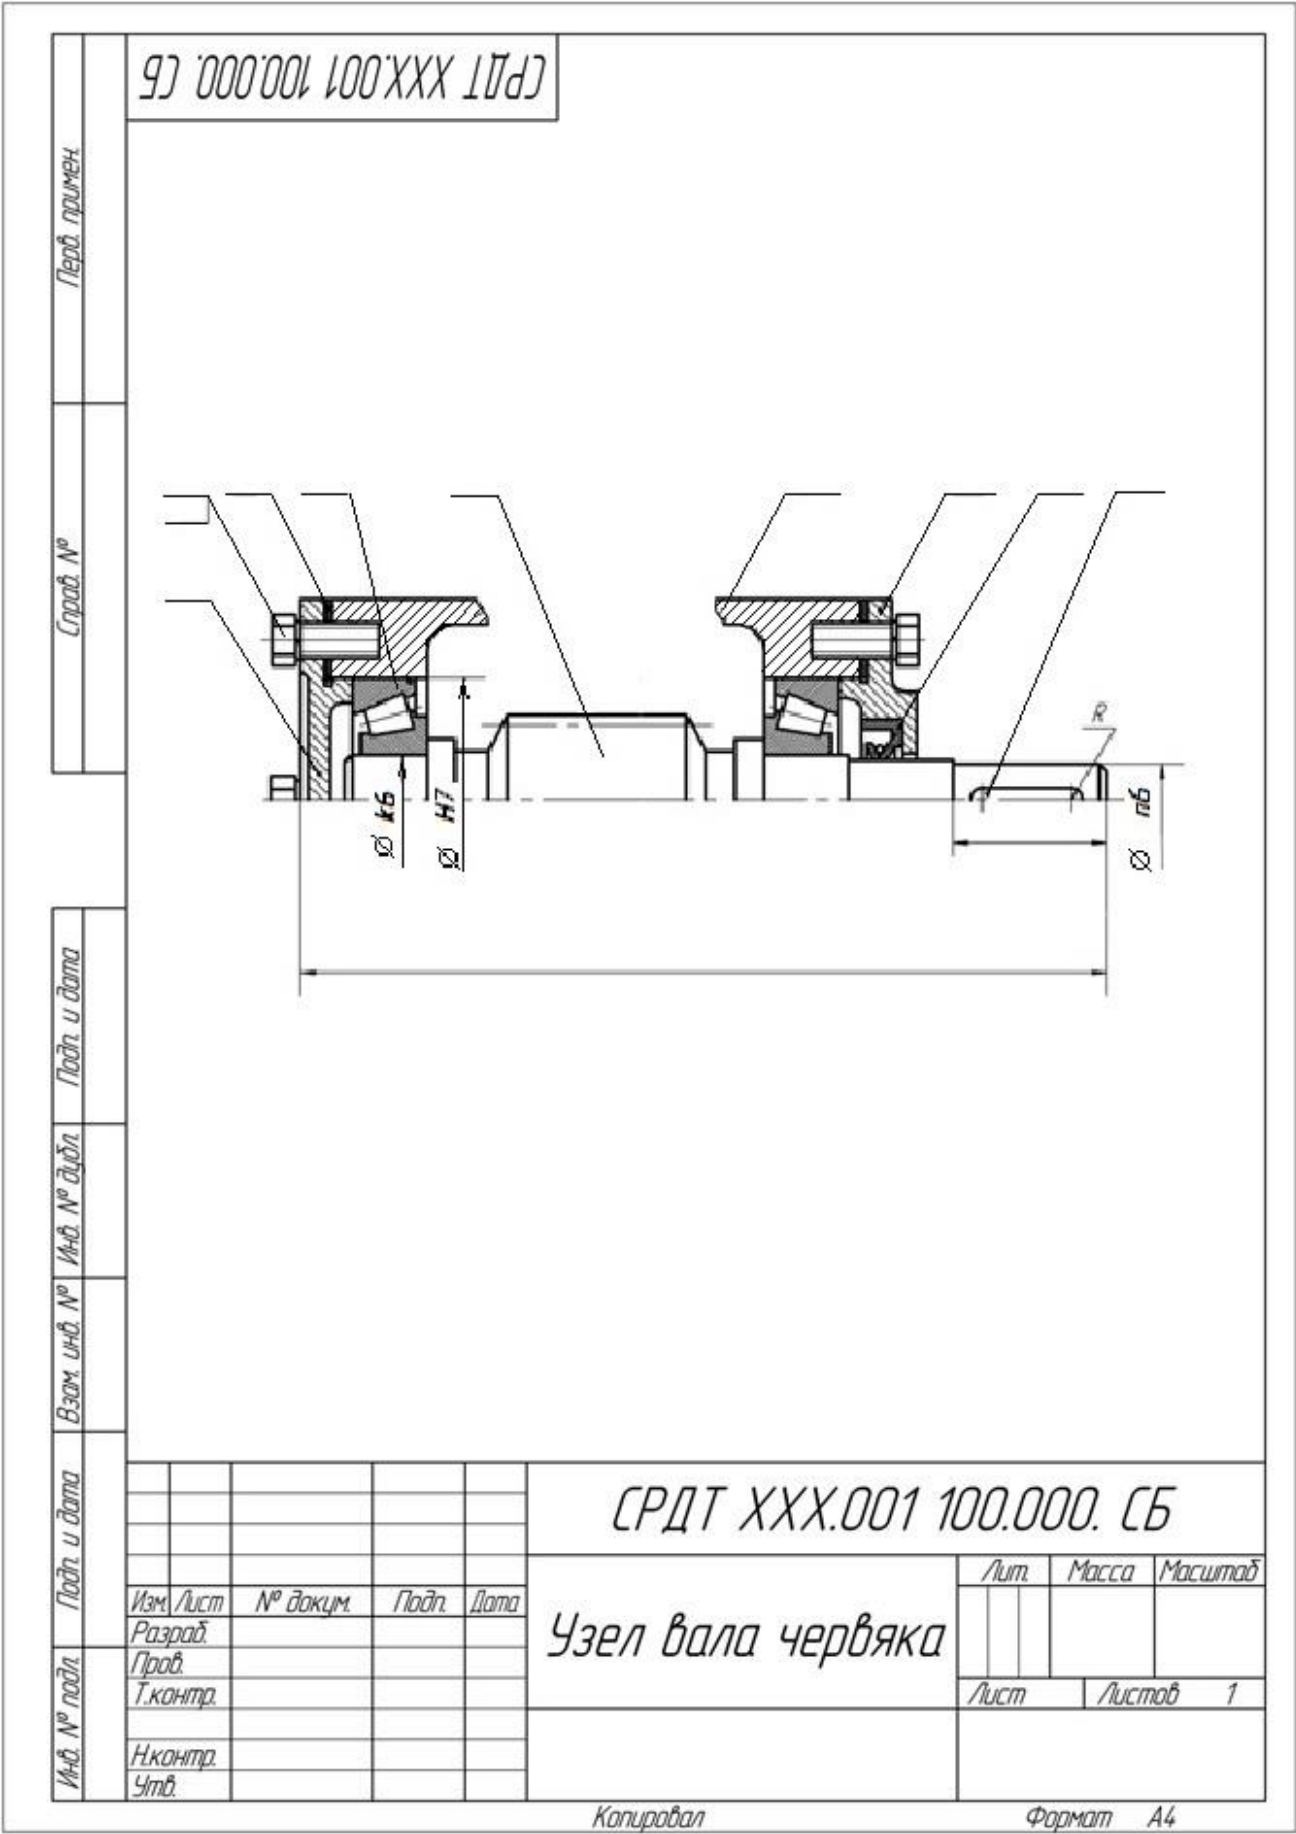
В.5. – Сборочный чертеж узла вала червяка
